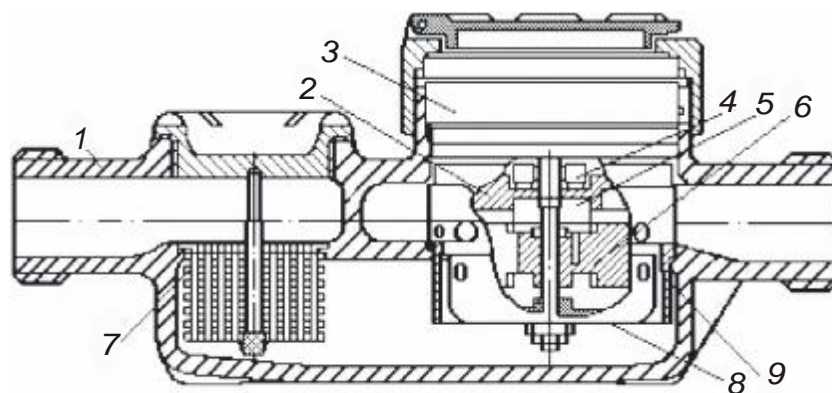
Разрез крыльчатого счетчика воды ВСКМ: 1 – корпус; 2 – разделительный диск; 3 – счетный меха-
